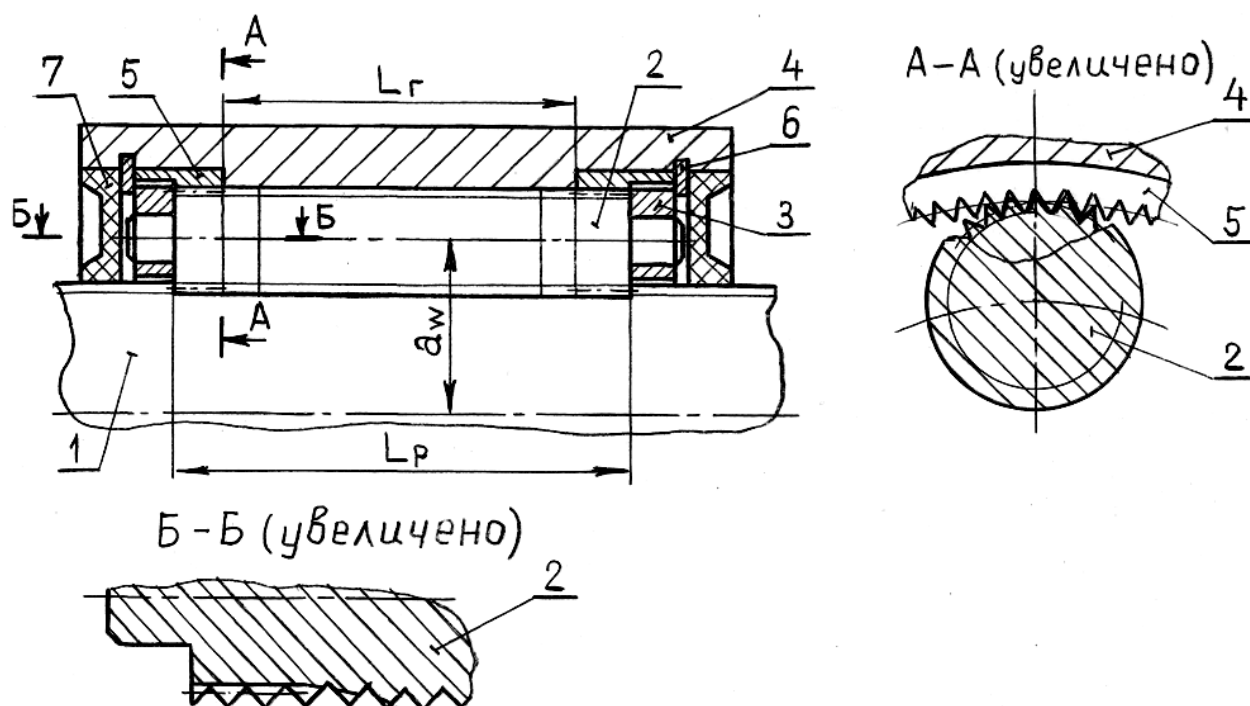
ПРВП: 1 – винт; 2 – резьбовой ролик; 3 – сепаратор; 4 – гайка;
